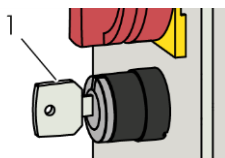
Schlüsselschalter unter dem Hauptschalter
